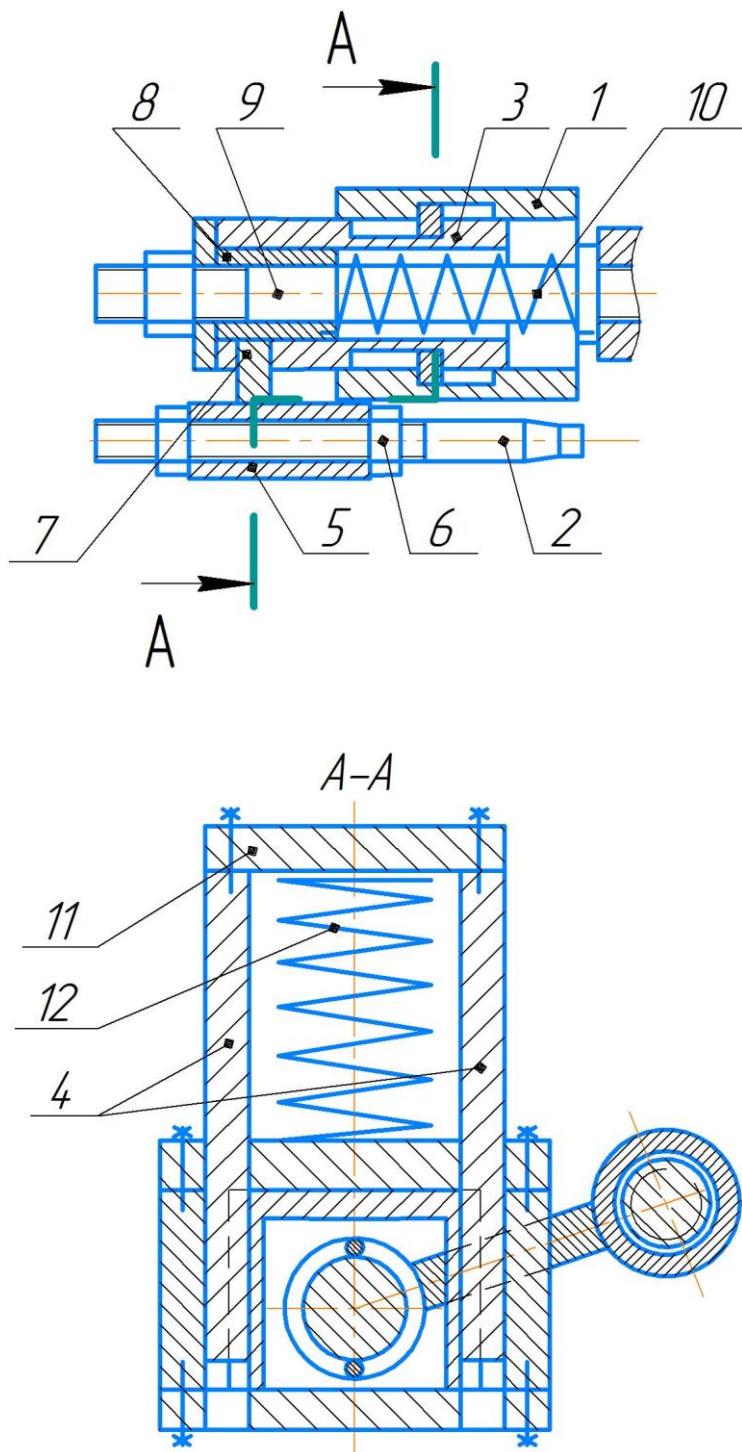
Механізм упору до штампу для відрізки сортового прокату зсувом
